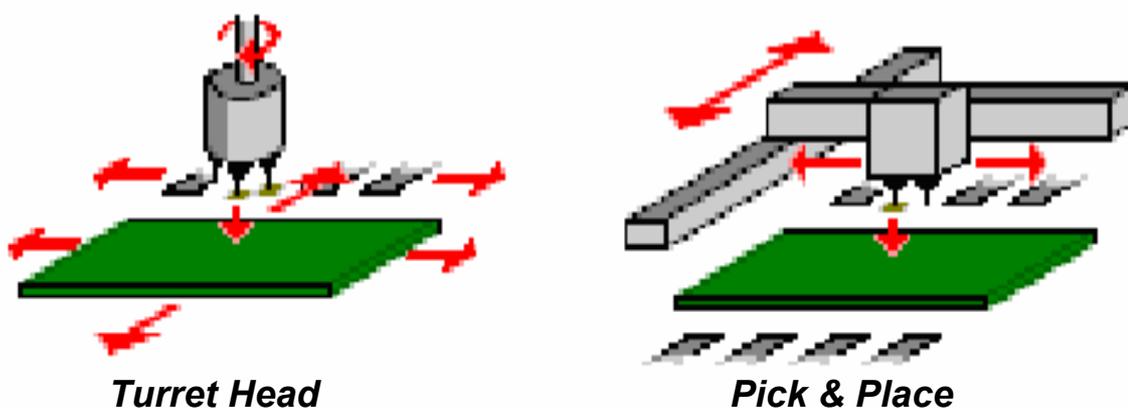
Método de funcionamento das cabeças posicionadoras das máquinas de inserção automática de componentes SMT ^[13]
